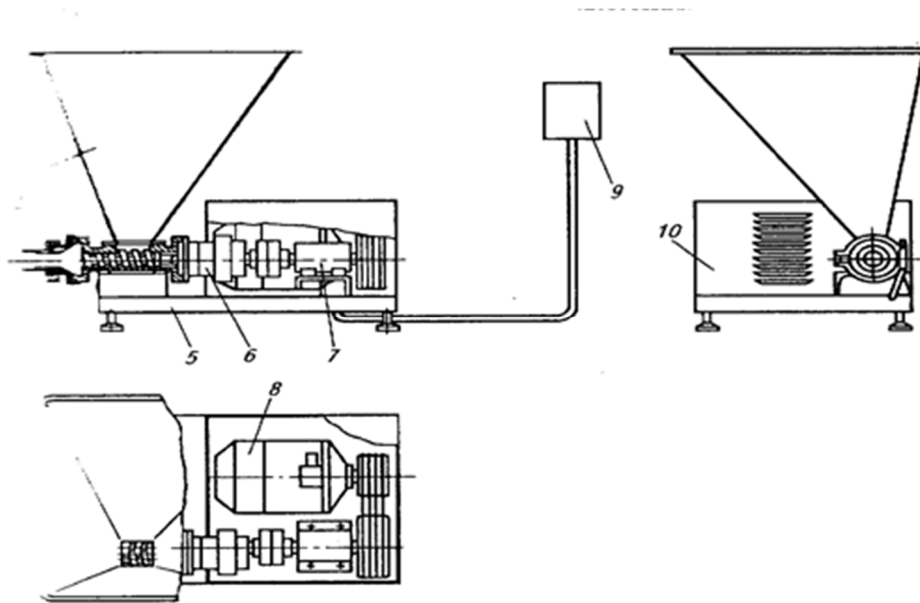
Установка А1-ФН-2К для непрерывного транспортирования по трубам фаршу:
